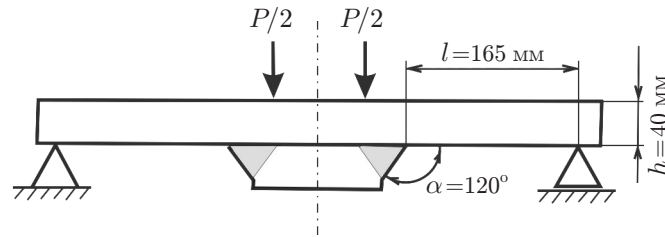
Модель сварного соединения с угловыми швами
